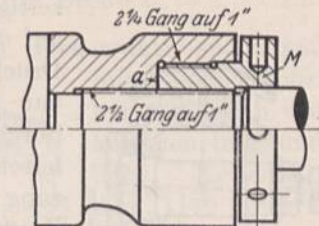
Befestigung der Stange durch Differentialgewinde.
